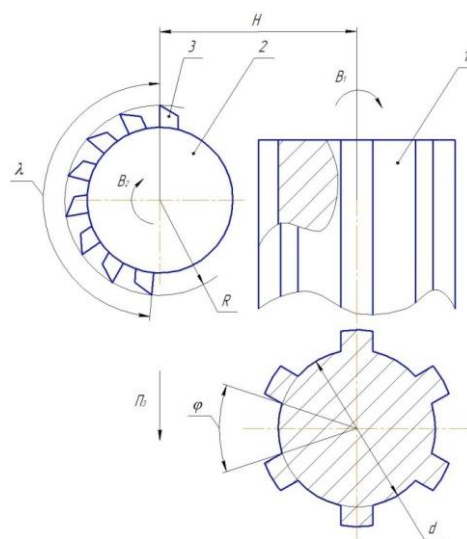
Схема формообразования поверхностей с зубчатым контуром
